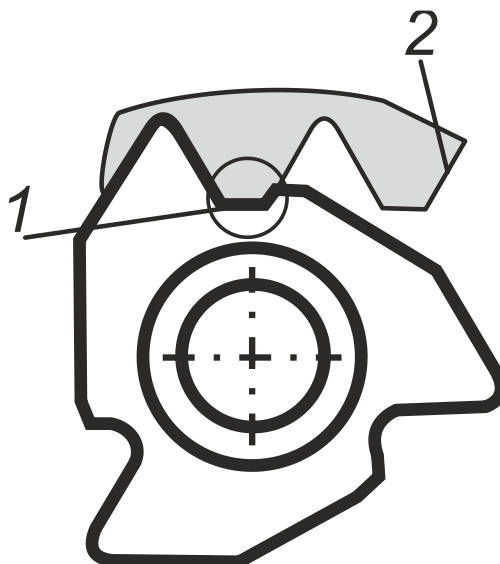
Схема формування різьби повнопрофільним різцем. Цифрами позначено: 1 – частина леза, яка формує гребінь різьби, 2 – різьба.
